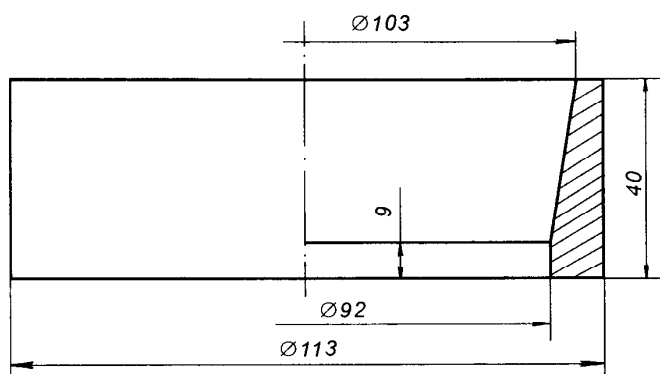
Установка поршня с кольцами в гильзу с помощью оправки
